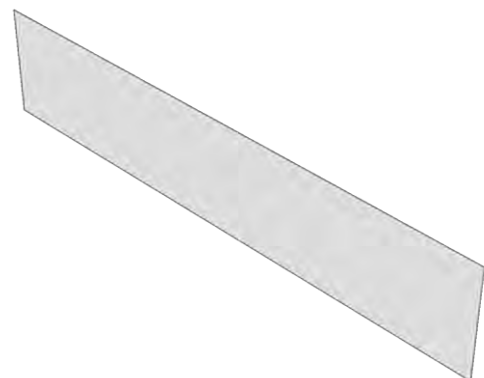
Эскиз детали верхнего и нижнего приспособления
